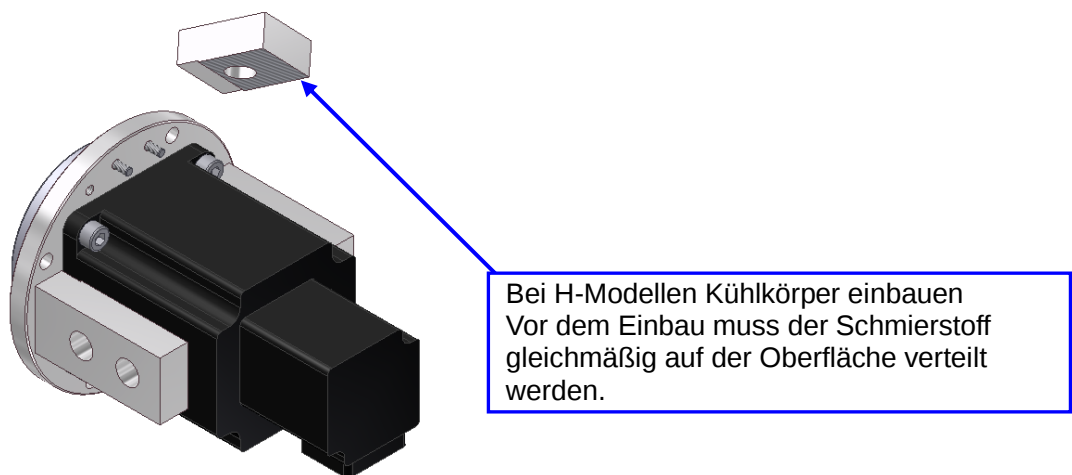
Explosionsdarstellung des Motors ohne Kühlkörper
